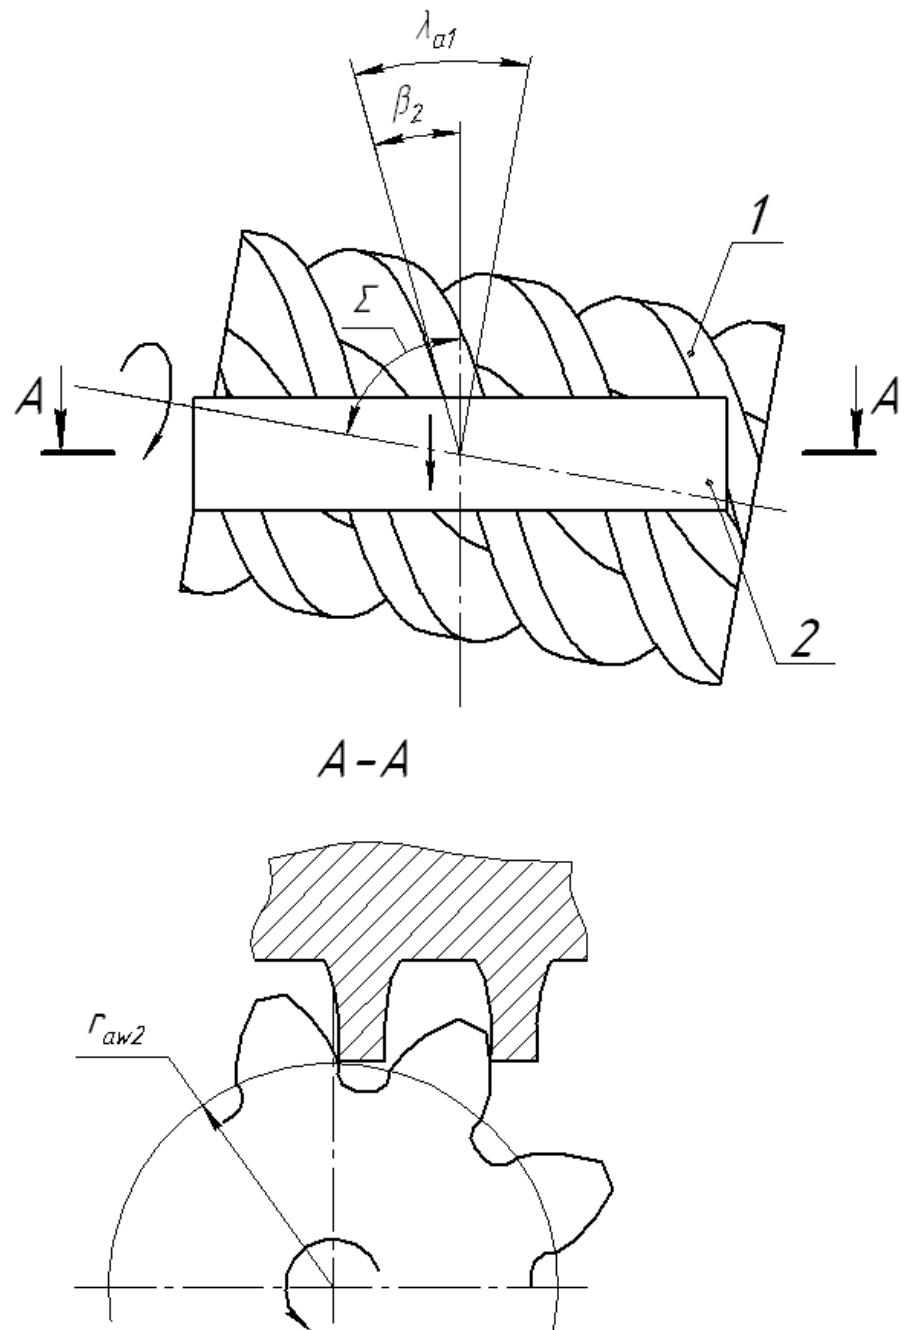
Схема работы инструмента червячного типа со сплошными винтовыми режущими кромками
